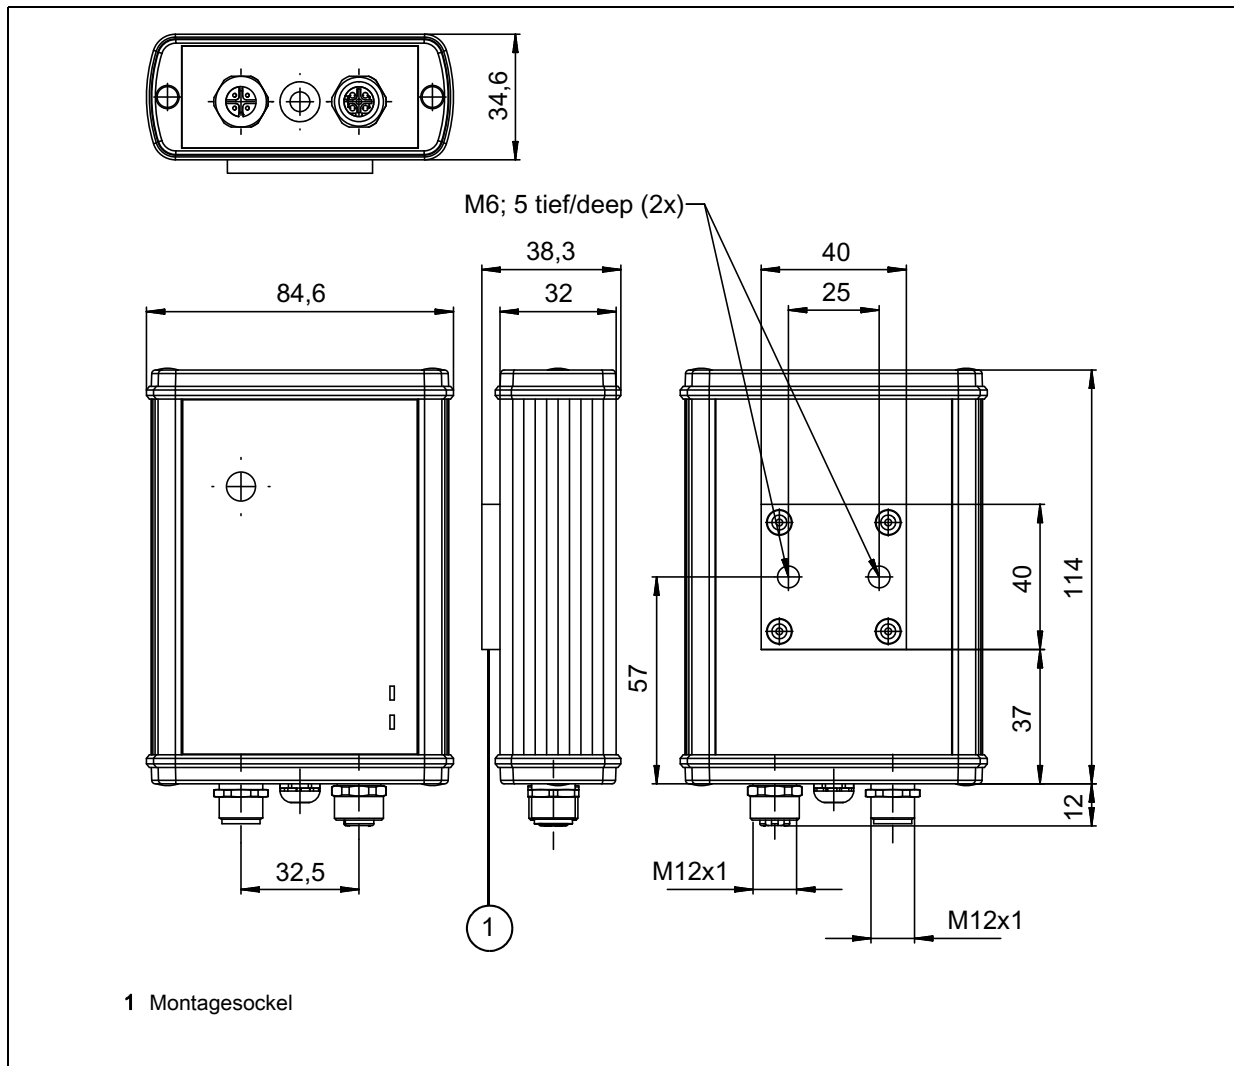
Mechanische Zeichnung des Gehäuses, Position des Montagesockels
